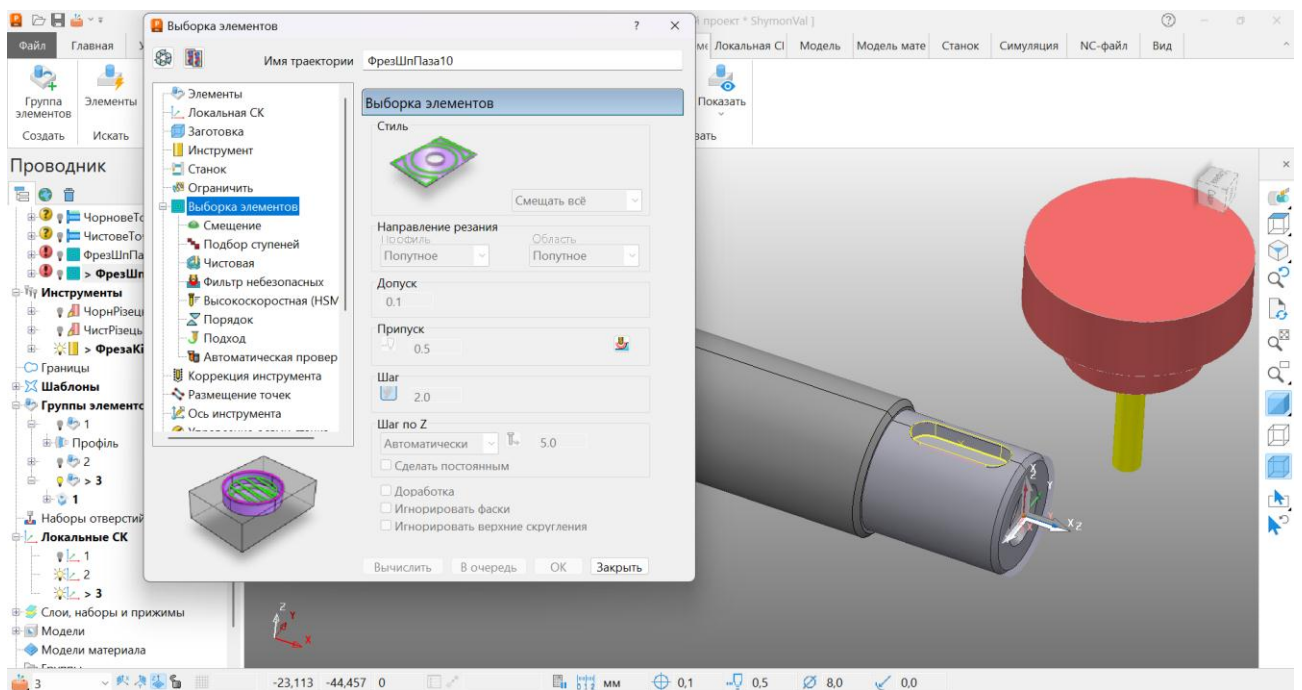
Проектування фрезерування шпонкового пазу
